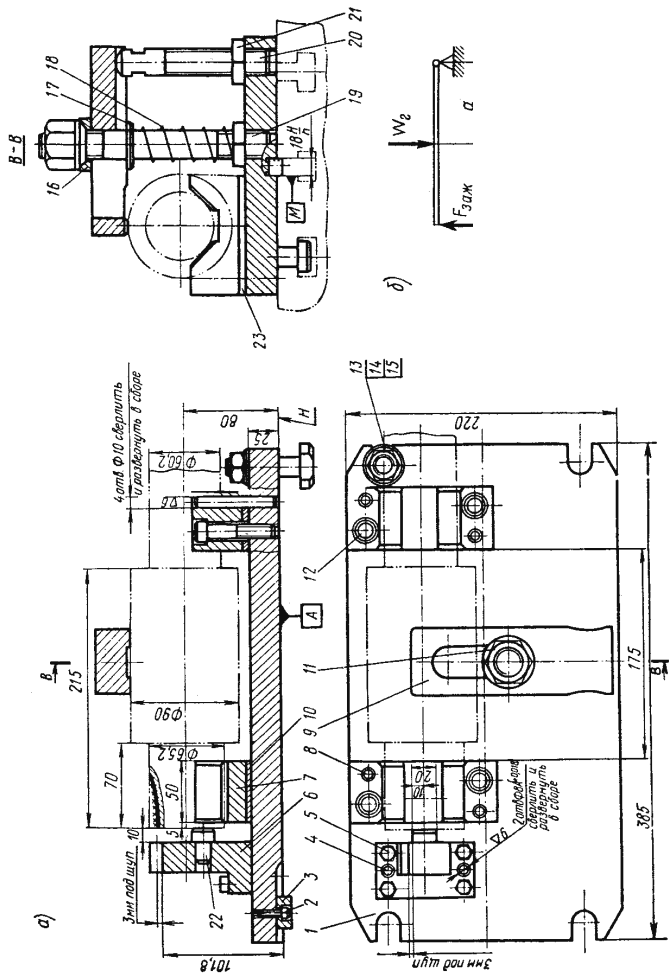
Приспособление для фрезерования шпоночного паза ступенчатого вала.
